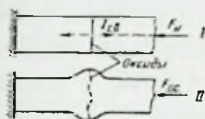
Схема образования соединения при стыковой сварке сопротивлением (F_n — начальное усилие; $F_{ос}$ — усилие осадки).
